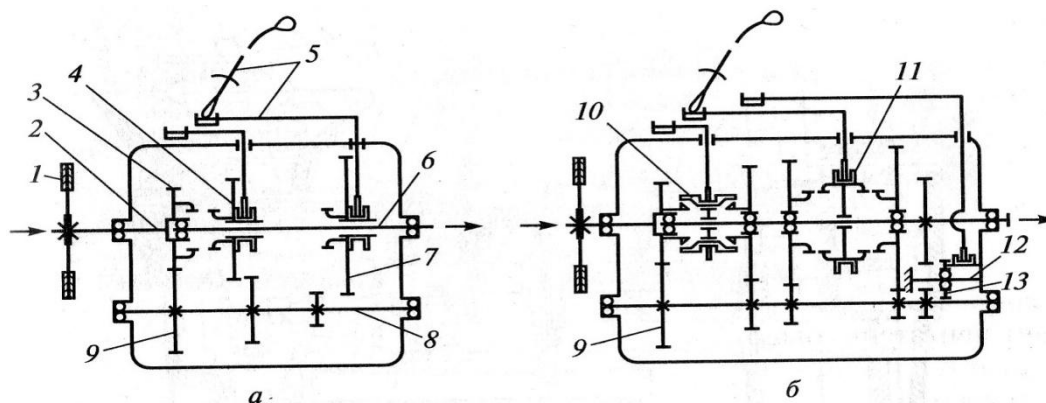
Схема устройства трехвальной коробки передач: а – с передвигными шестернями; б – с шестернями постоянного зацепления; 1 – ведомый диск сцепления; 2 – ведущий вал; 3,9 – шестерни постоянного зацепления; 4,7 – передвигные шестерни; 5 – механизм переключения; 6 – ведомый вал; 8 – промежуточный вал; 10 – синхронизатор; 11 – муфта легкого включения; 12 – ось шестерни заднего хода; 13 – шестерня включения заднего хода
